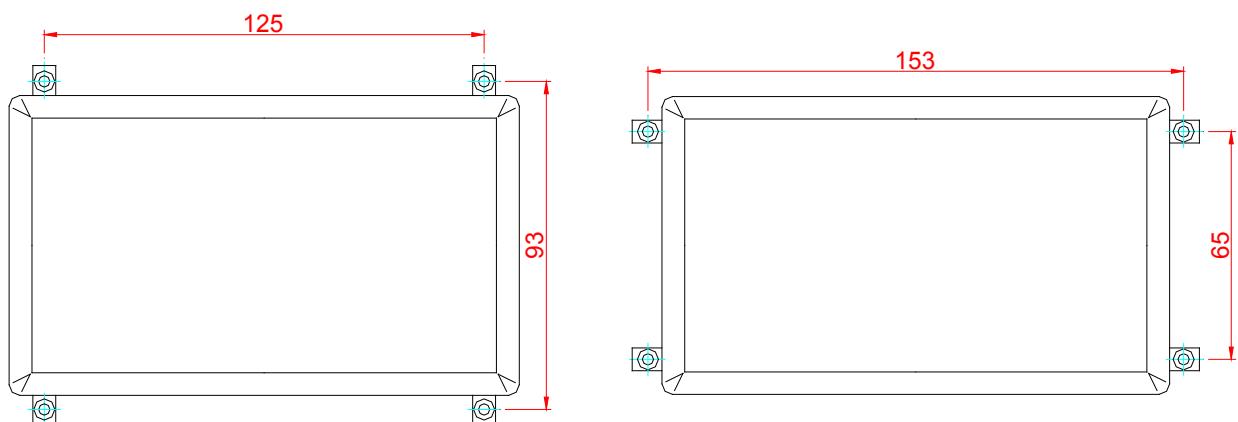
Montage - Bohrmaße (alle Maße in mm)
